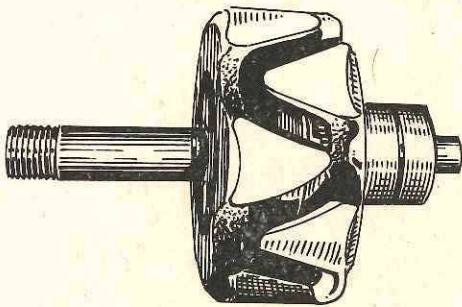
Erregerrotor einer Bosch-Drehstromlichtmaschine
